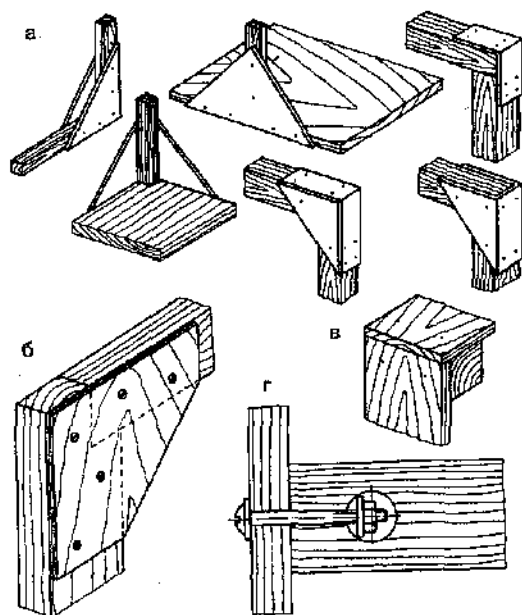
Соединение деталей в прямой угол: а — металлическим угольником; б — фанерным угольником; в — деревянным бруском; г — стяжным болтом
